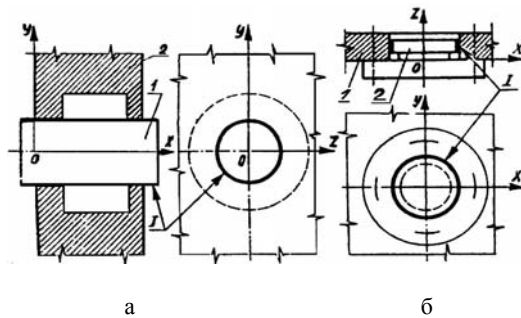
Базирование заготовок (деталей) с использованием цилиндрических базовых поверхностей:
